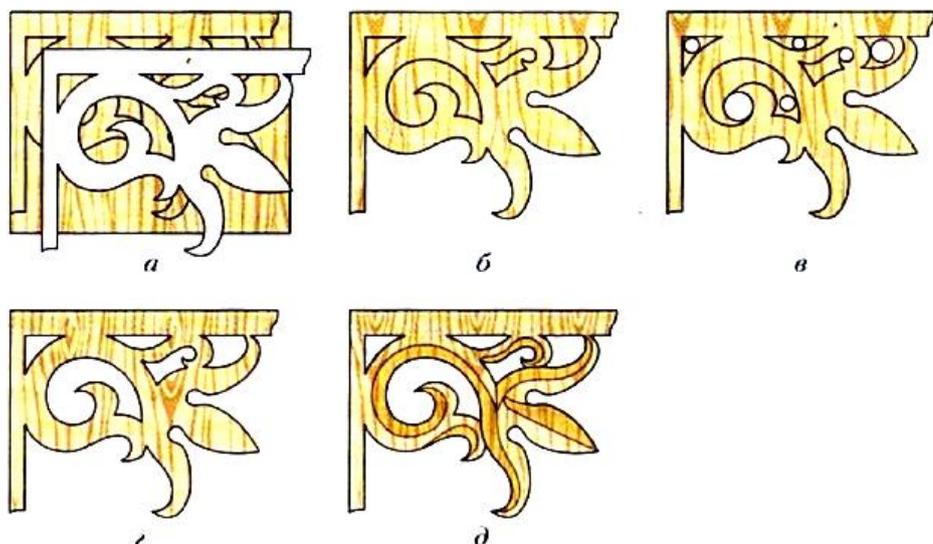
Технология выполнения ажурной резьбы по дереву: а — нанесение рисунка на заготовку с помощью шаблона; б — выпиливание внешнего контура; в — сверление отверстий; г — выпиливание внутренних контуров; д — отделка формы и зачистка
